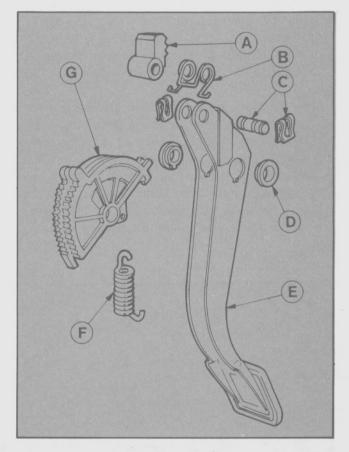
Pedal de embrague y mecanismo de ajuste automático.
